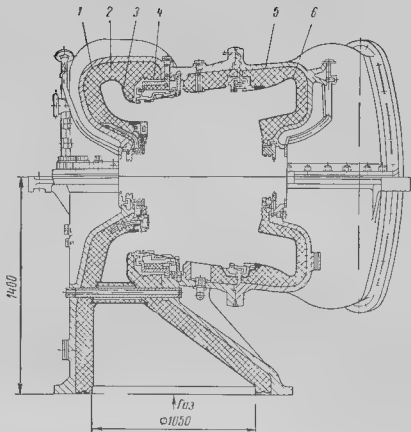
Корпус газ. турбины ГТ-700-5 НЗЛ
